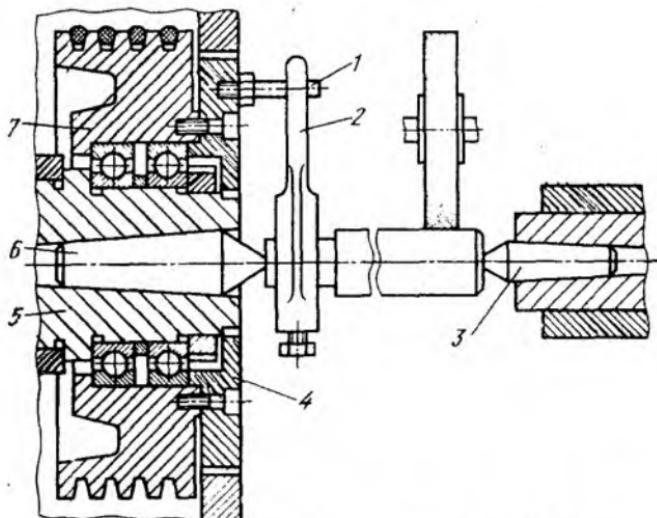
Схема установки заготовки в упорных центрах круглошлифовального станка:
